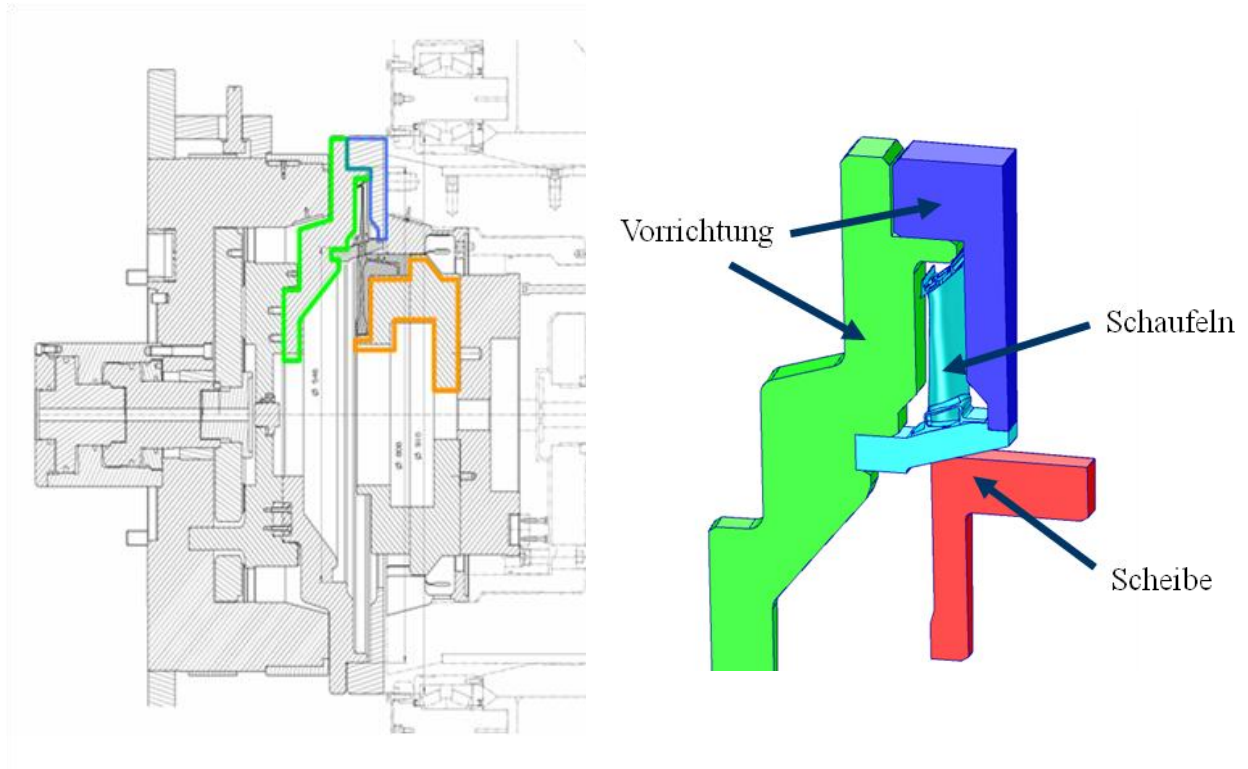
Vorrichtungskonzept für die Kegelschweißung
